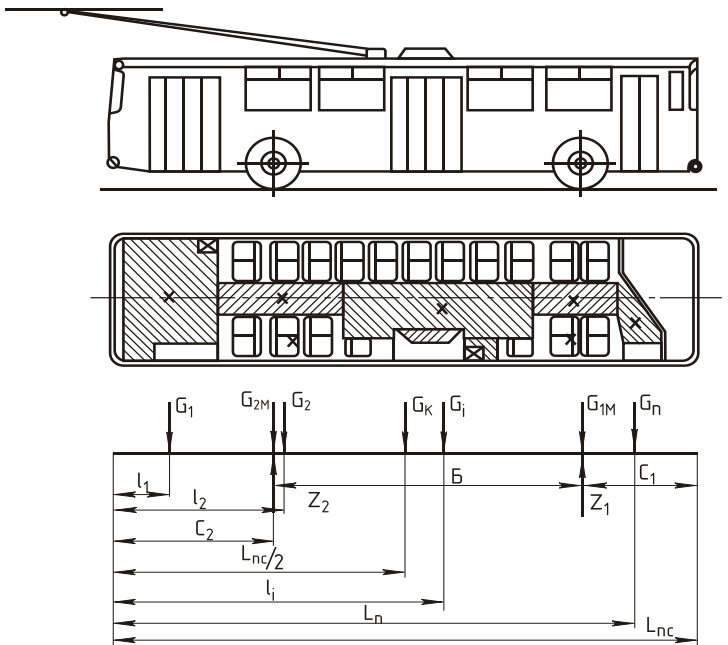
Планировка салона и расчетная схема нагрузок двухосного троллейбуса
